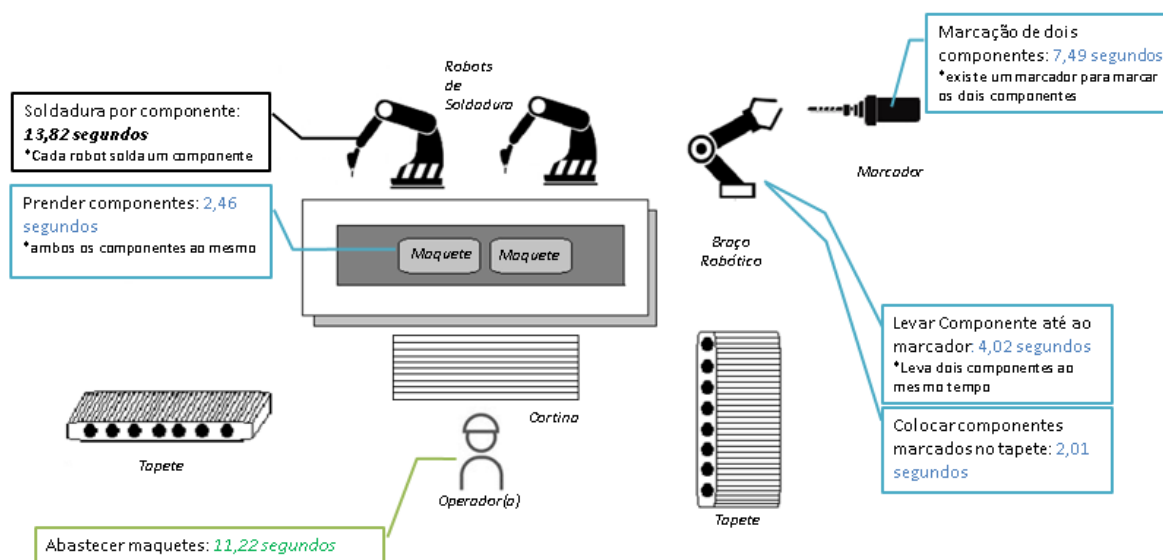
Representação da célula de soldadura, com a eliminação da rotação
